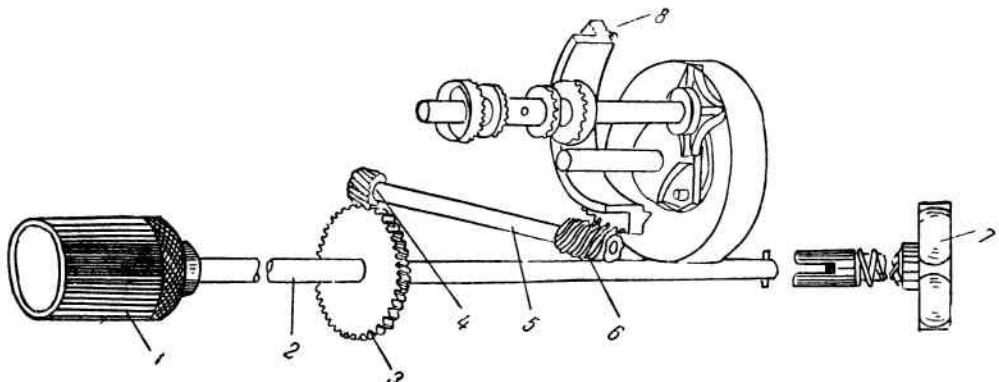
Кинематическая схема передачи движения при установке кадра в рамку:
